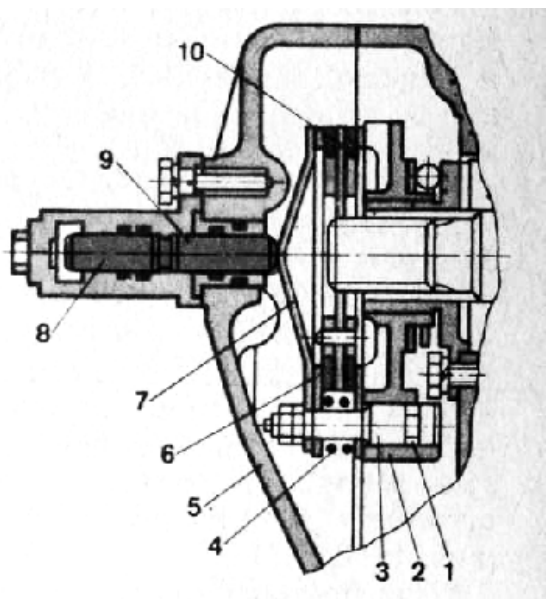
Тормозок первичного вала коробки диапазонов скоростей:
